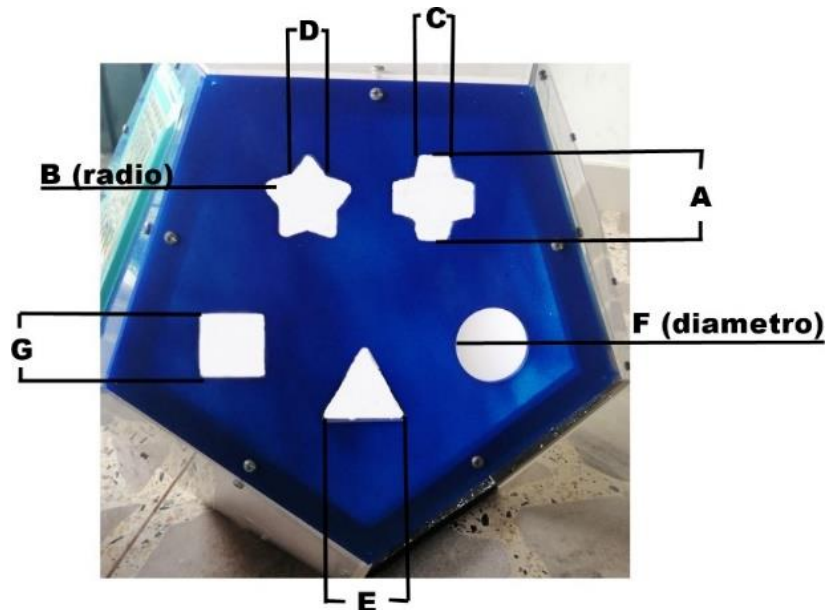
Dimensiones de la sección insertar figuras geométricas (autoría propia).
